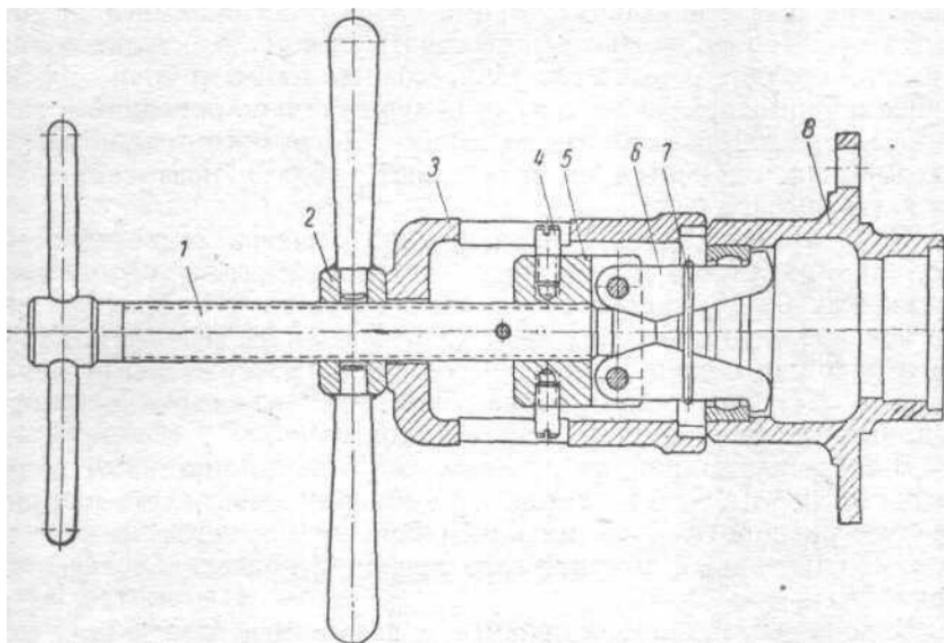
Съемник для выпрессовывания наружного кольца внутреннего подшипника ступицы переднего колеса:
